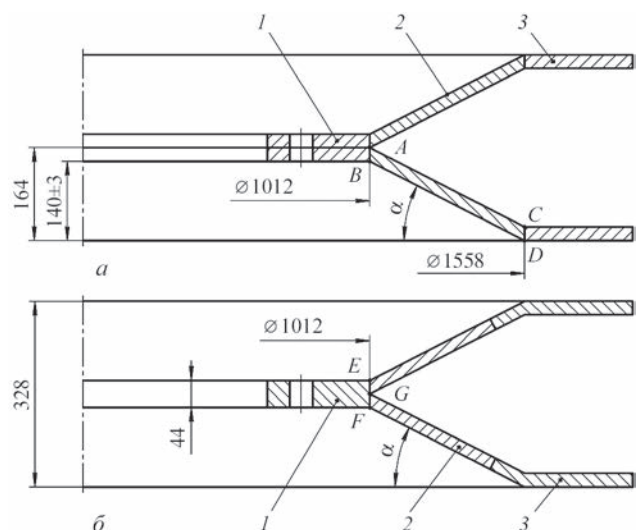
Первый (а) и второй (б) варианты выполнения сварного диска рабочего колеса дымососа: 1 — кольцо; 2 — обечайка; 3 — окантовка
